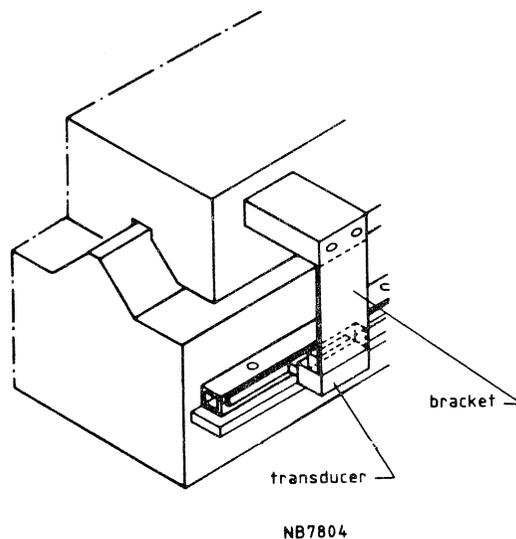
1 Befestigungsbrücke (Beispiel)
